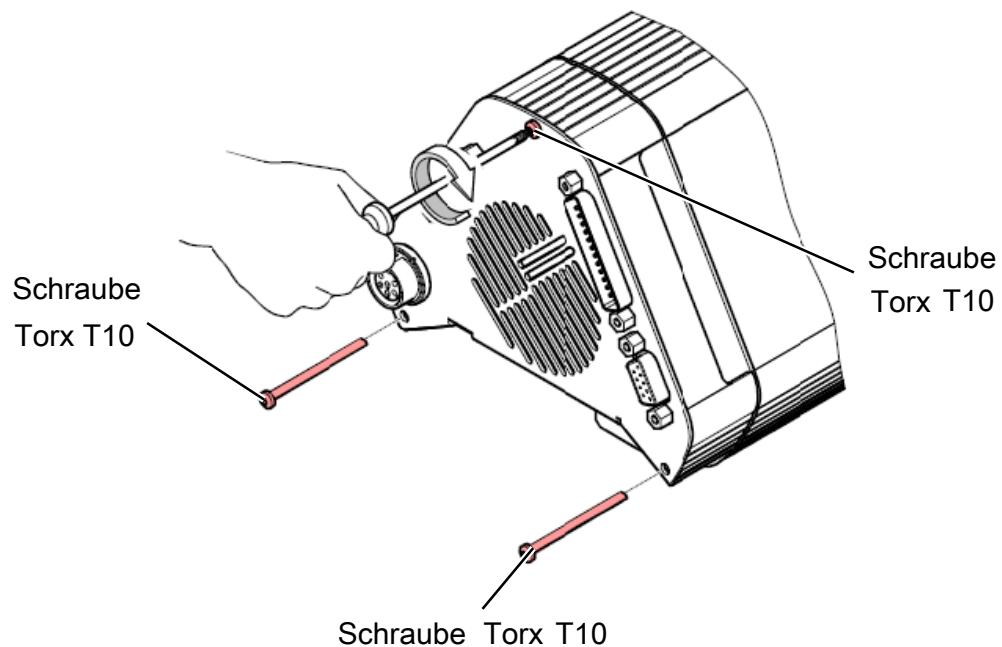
CHLD-Sensor: Modul IO 220 entfernen
